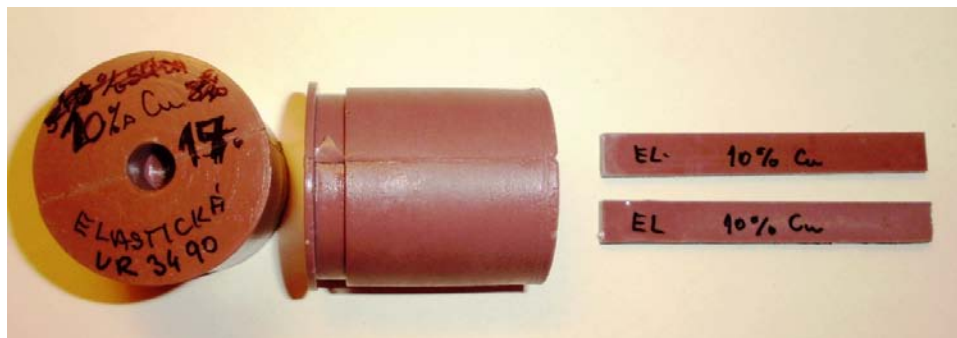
a) Balení pryskyřice b) Odformované prototypy z UR 3490
